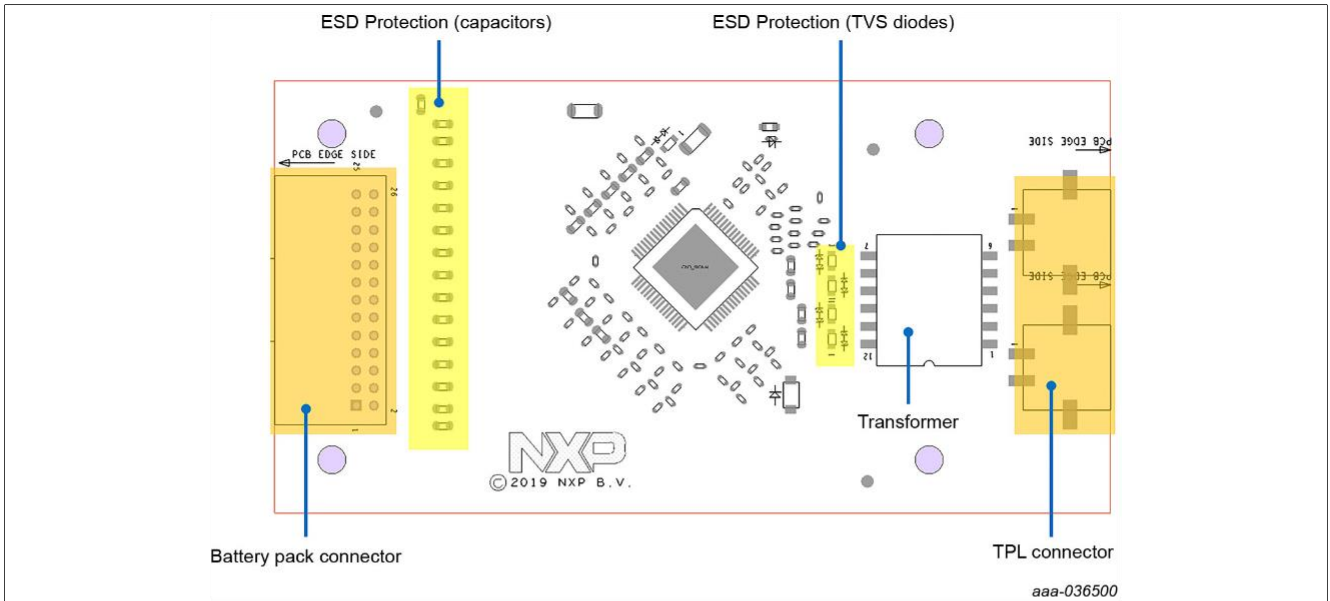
区域 3 - PCB 顶面上的 ESD 保护
